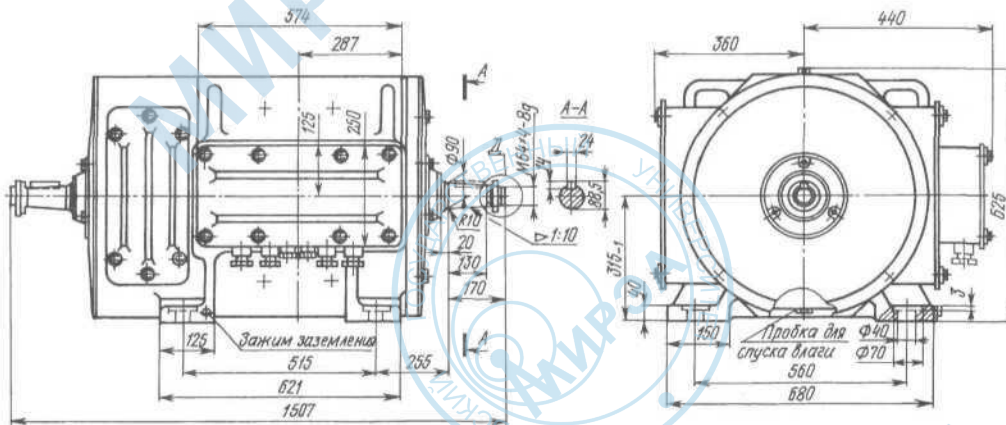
Габаритные, установочно-присоединительные размеры двигателя без тормоза тип "ДПМ 62"
